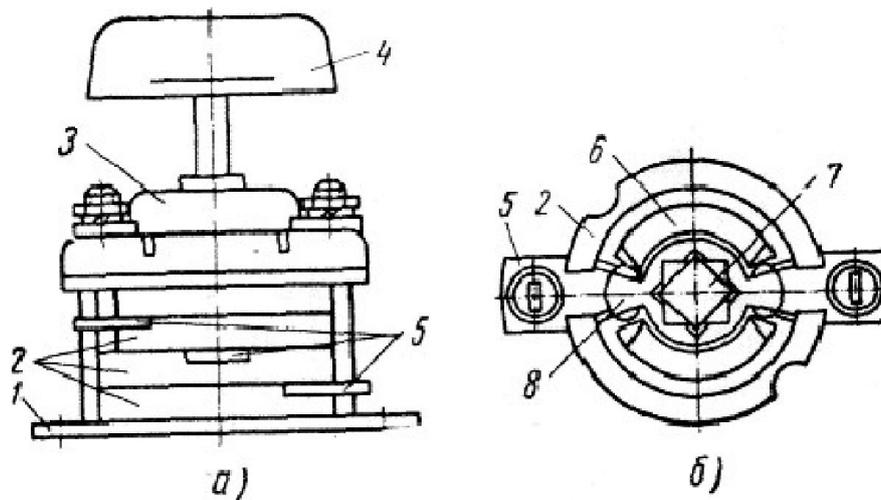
Пакетний вимикач ПК: а – загальний вигляд, б – секція (пакет); 1 – скоба та стяжні шпильки, 2 – ізолятор, 3 – кришка, 4 – рукоятка, 5 – нерухомі контакти, 6 – іскрогасильна фіброва шайба, 7 – чотириохгранна вісь, 8 – пружинячий рухомий контакт.
